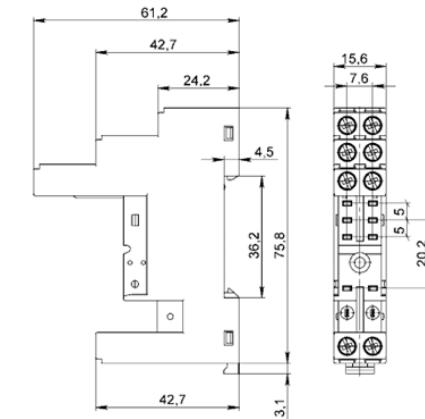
Габаритные, установочные и присоединительные размеры розетки OptiRel G RR95-02
